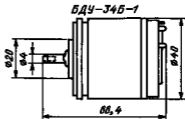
Габаритные и установочные размеры датчиков угла БДУ-34Б-1, БДУ-38-И
